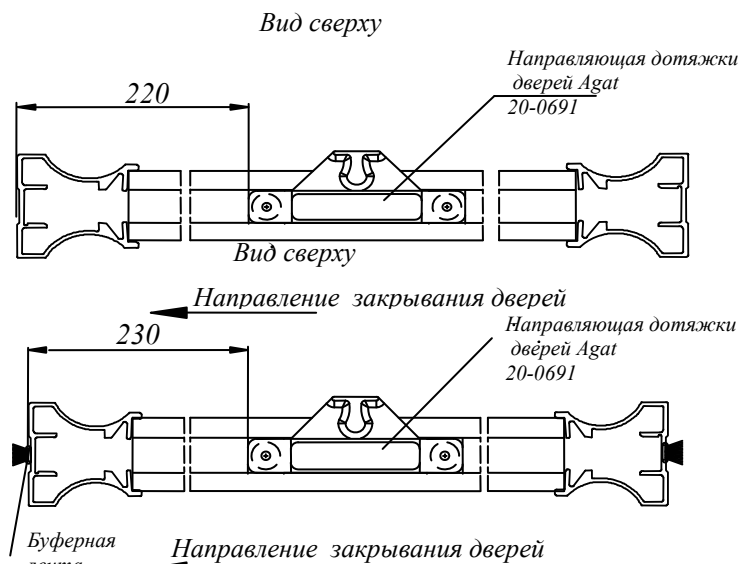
Крепление зацепки к верхнему горизонтальному профилю
